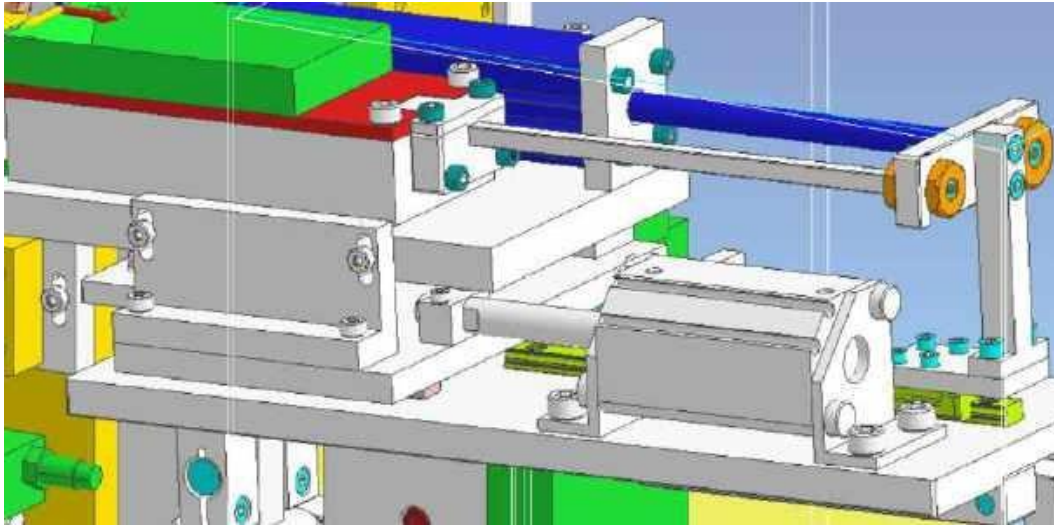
7 Spring Jig Assembly RCF N100 With Collaborative Robot- Front View
